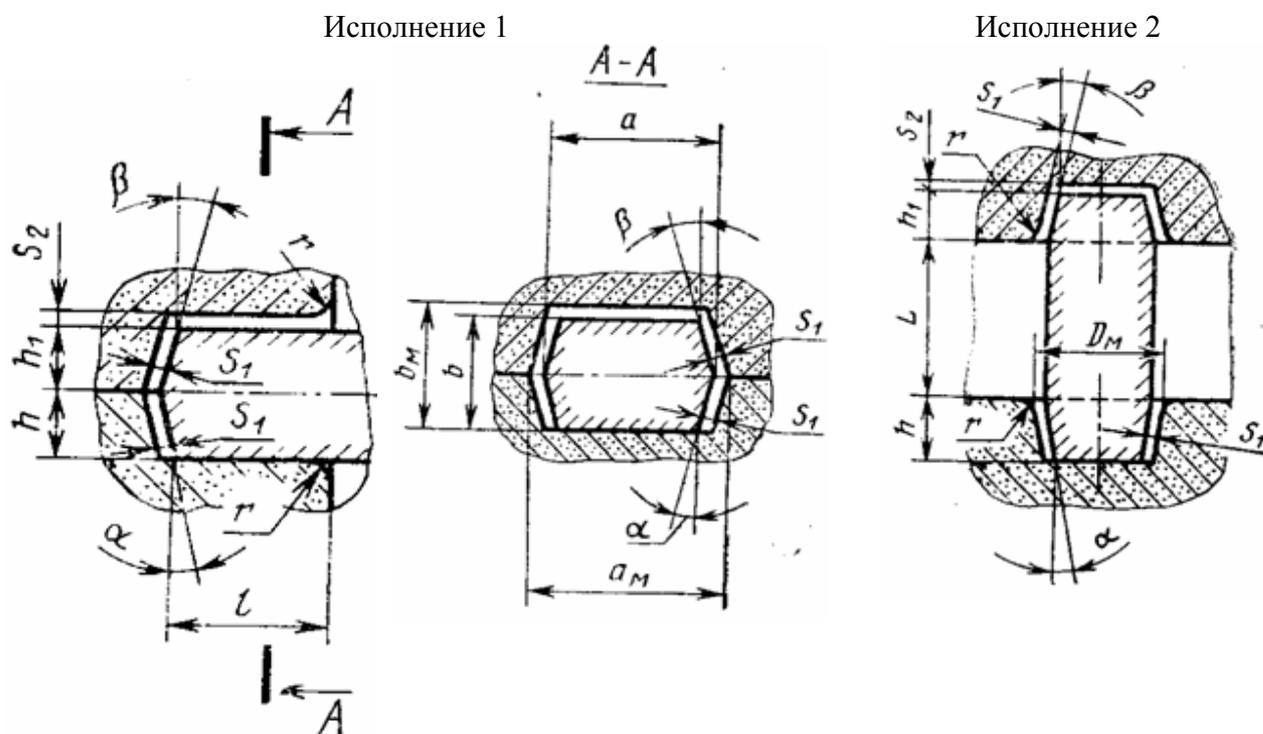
Радиусы скруглений (r) от основной к знаковой формообразующей поверхности
